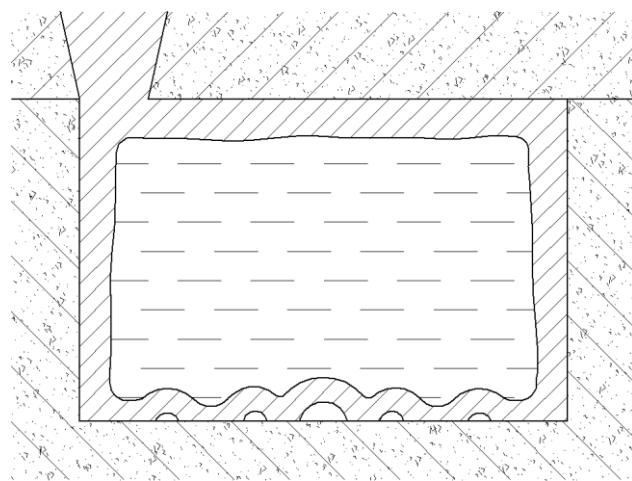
Газова шорсткість на поверхні виливка
